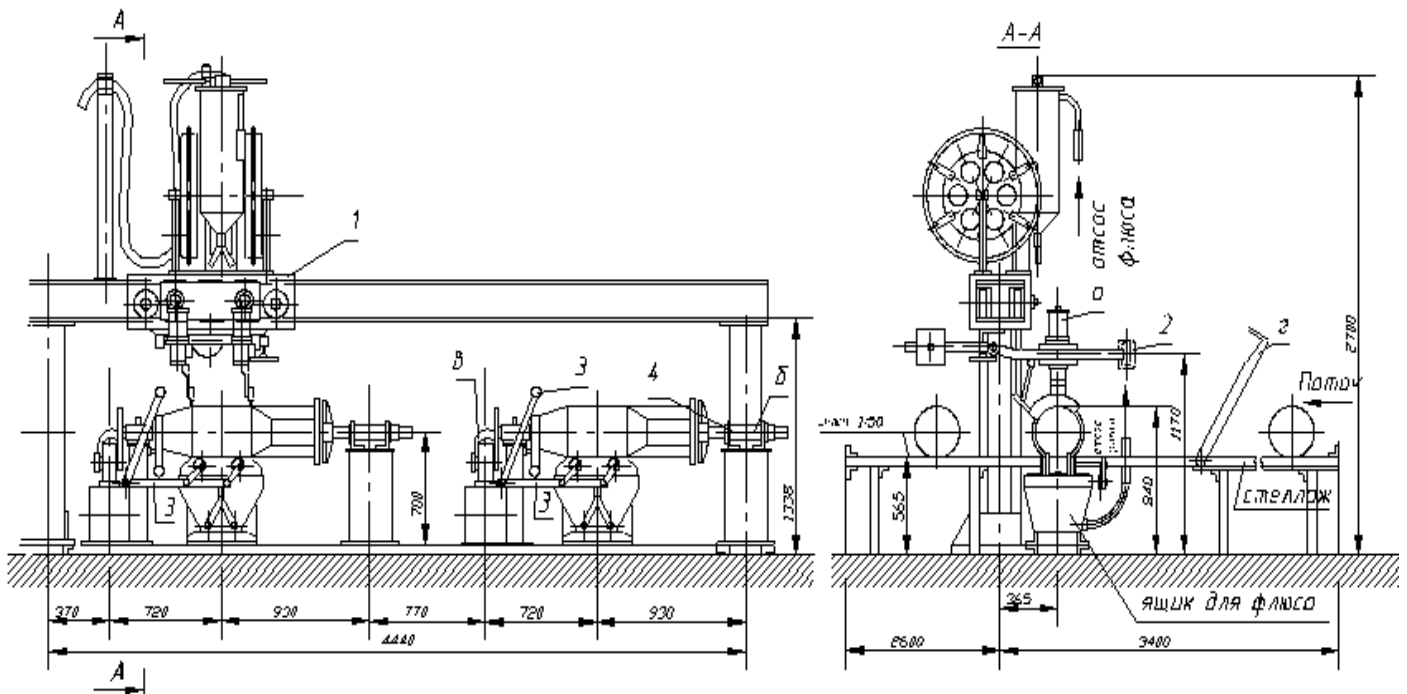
Установка з двохстojковими центровими обертачами для автоматичного зварювання кільцевих швів
